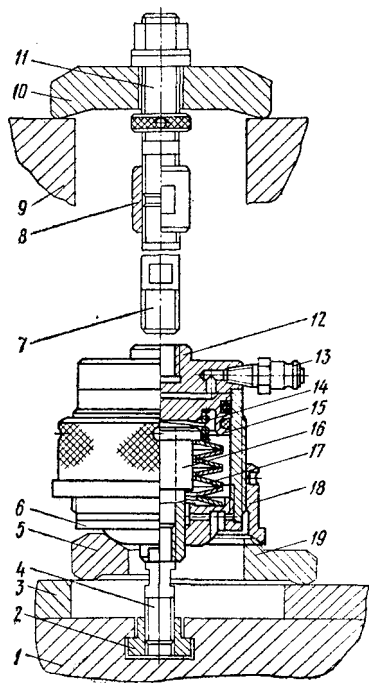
Цилиндр с тарельчатыми пружинами тянущего типа
